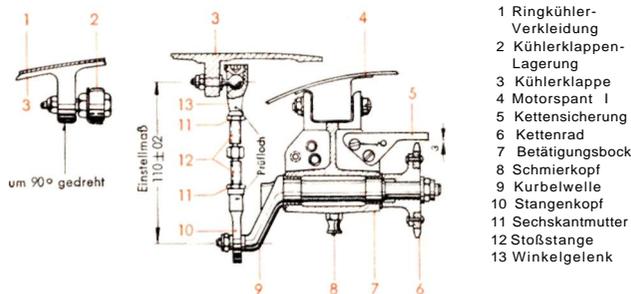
Betätigungsbock für Kühlerklappe (bei Blechspant)
